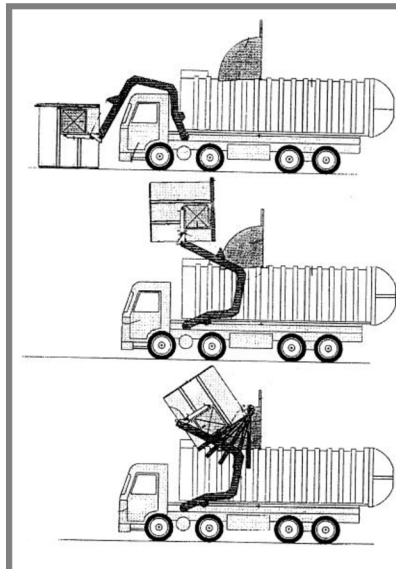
Mechanismus otevírání kontejneru - šikmá ramena [18]
